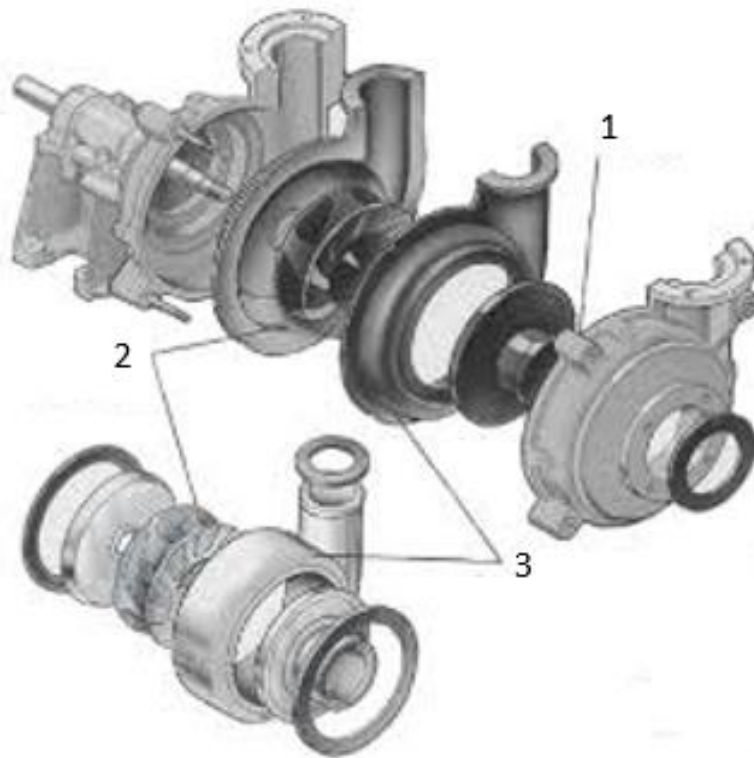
Схема шламового насосу: 1 – зовнішній корпус;
